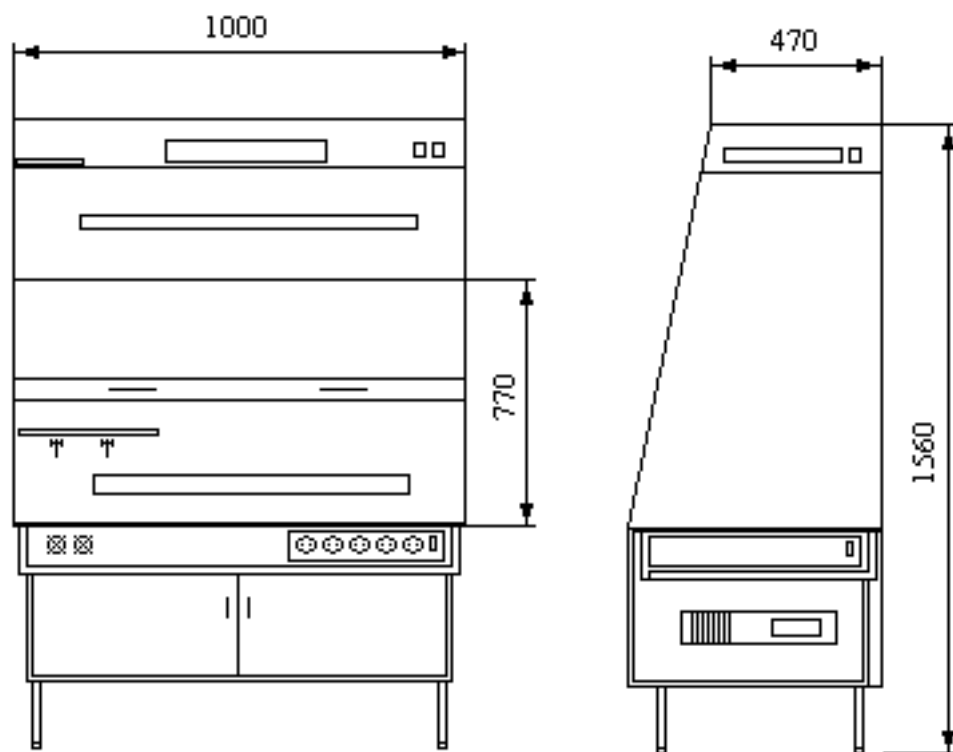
Витяжна шафа для виготовлення печатних плат
